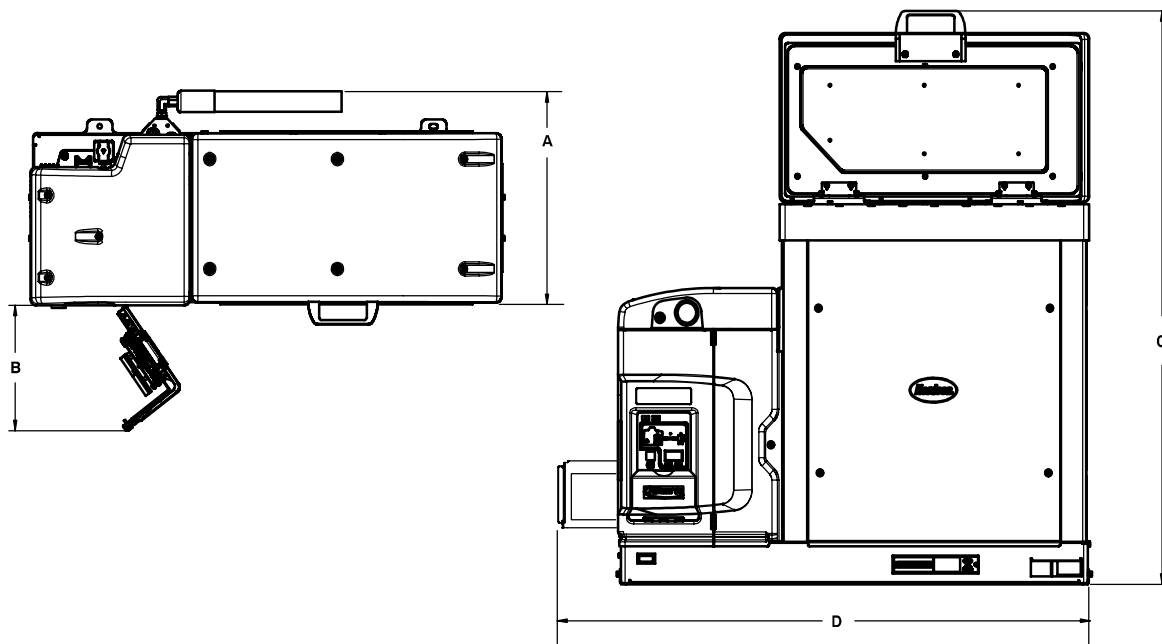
Spazio minimo per l'installazione (visione dall'alto e di lato)
